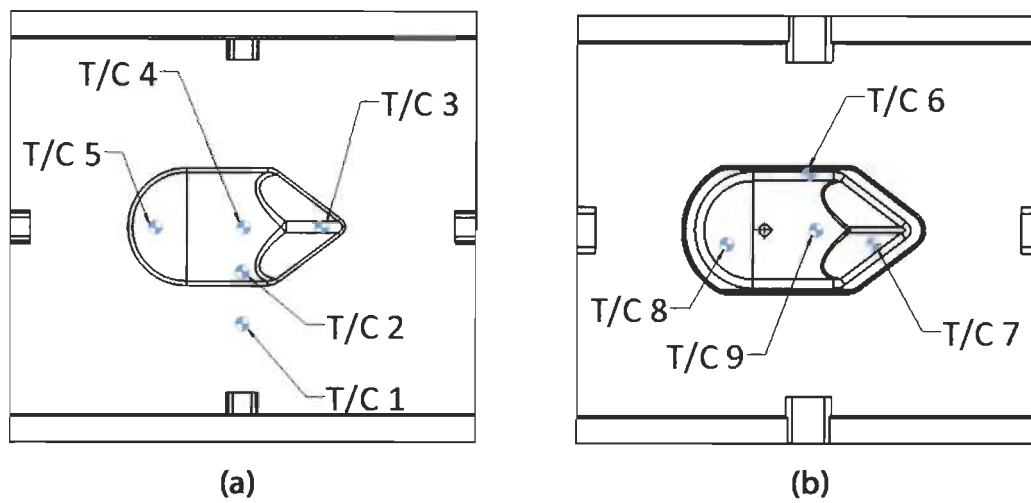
Position des thermocouples dans le moule. (a) Matrice et (b) poinçon.
